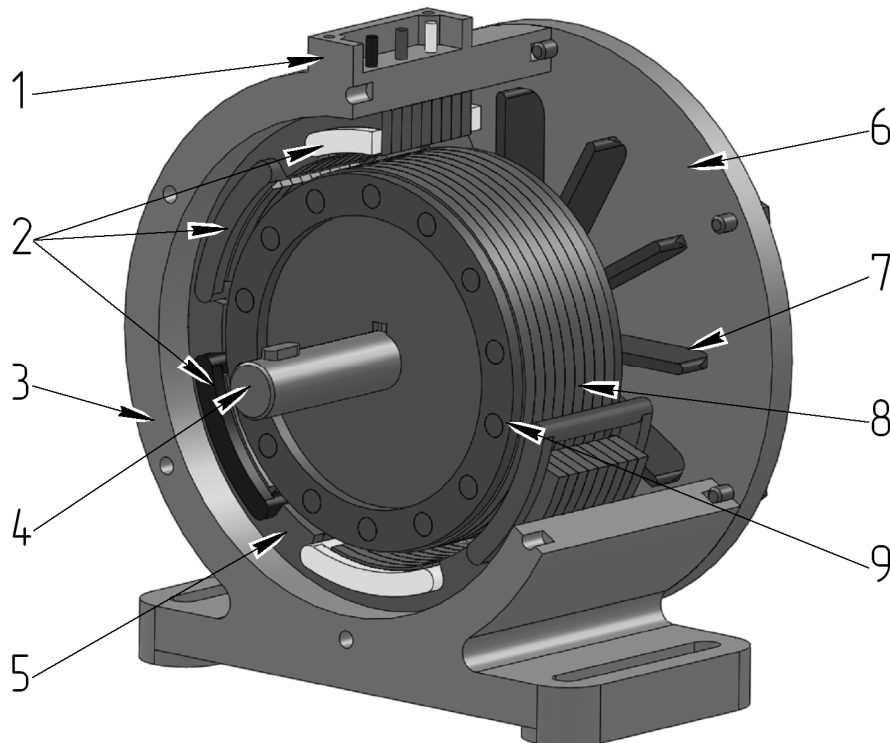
Конструкция асинхронного электродвигателя: 1 – клеммник; 2 – трехфазная обмотка; 3 – станина; 4 – вал; 5 – магнитопровод статора; 6 – крышка с подшипниковым узлом; 7 – вентилятор; 8 – магнитопровод ротора; 9 – короткозамкнутая обмотка
